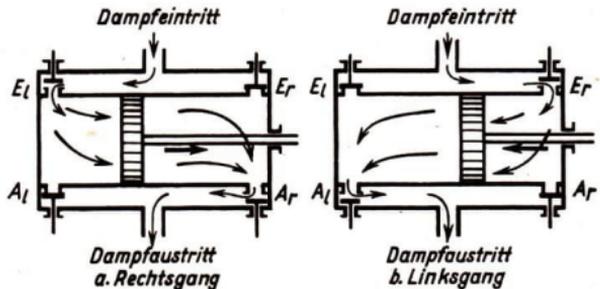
Einfache Ventilsteuerung. E Eintritts-, A Austrittsventile
